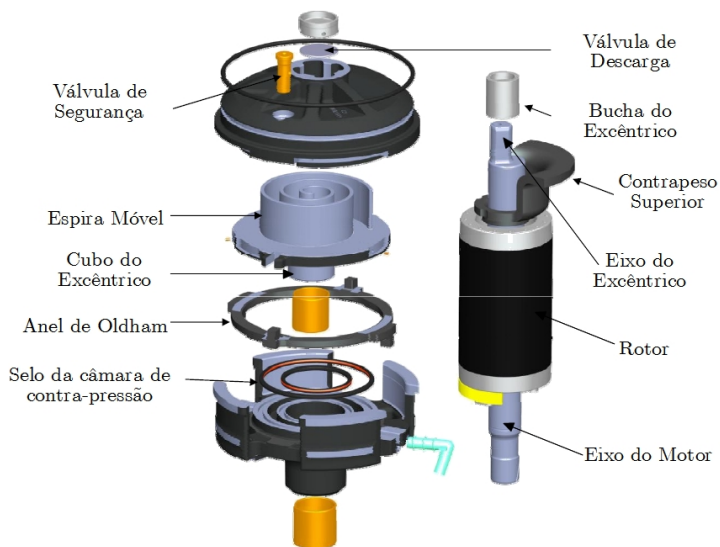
Vista explodida de um compressor scroll (reproduzido de DANFOSS, 2008).
